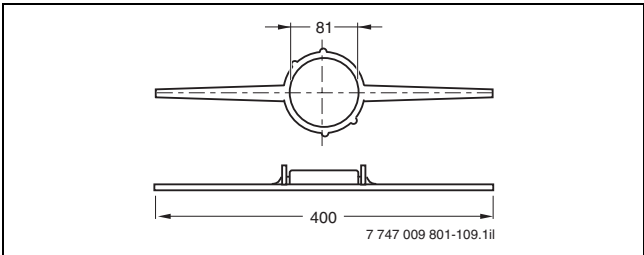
Abstandhalter für Abgasleitung im Schacht (Maße in mm)
